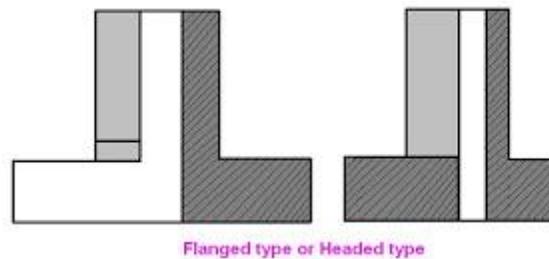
Renewable Bushes. Fuente: American Machinist
